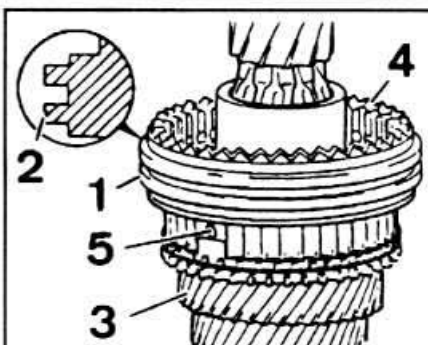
Установка скользящей муфты синхронизатора III и IV передач:
